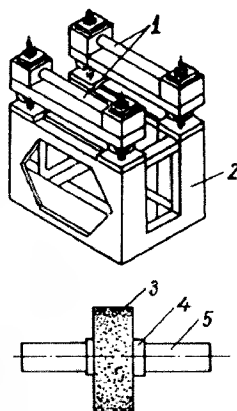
Схема балансировочного станка с параллельными валиками:
